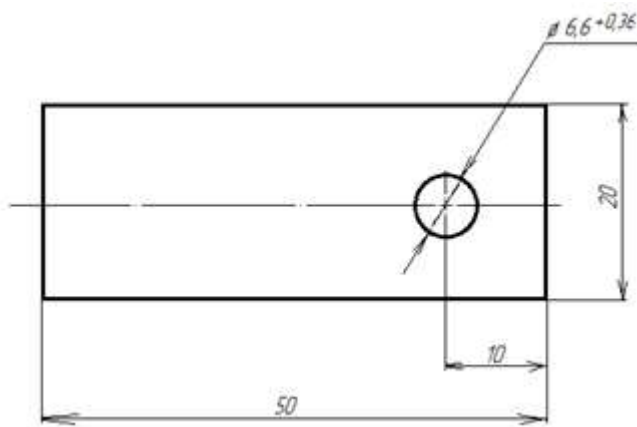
Бирка о проведении ремонта редуктора
